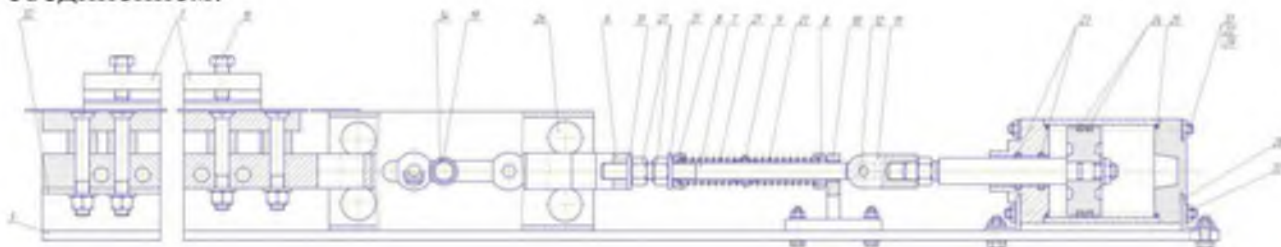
Экспериментальный сварочный модуль
